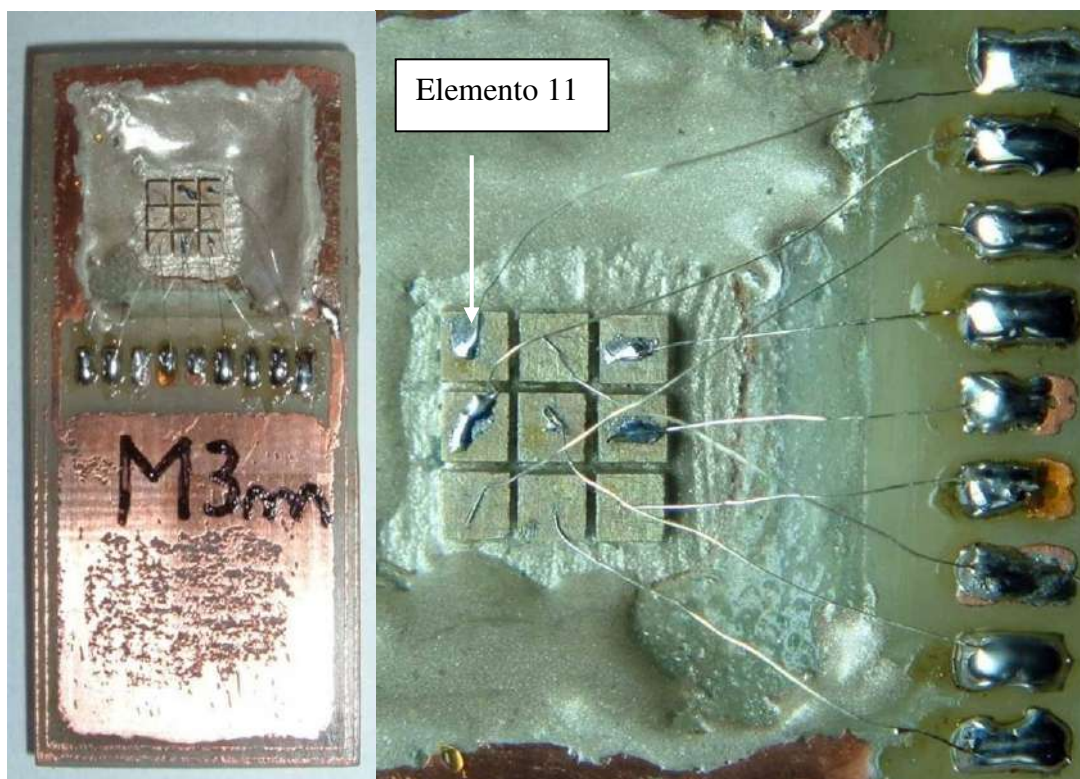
Matriz M3m soldada e montada na base de encapsulamento. Esquerda. Visão geral. Direita. Detalhe da soldagem da fiação entre os elementos e ilhas de cobre. Observar alguns cruzamentos aéreos dos fios.
